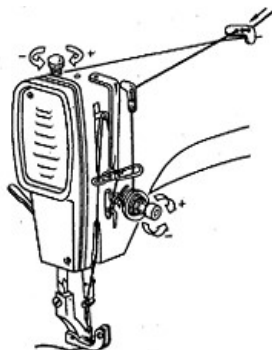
Схема регулювання величини натягу верхньої та нижньої ниток в швейній машині човникового стібка
